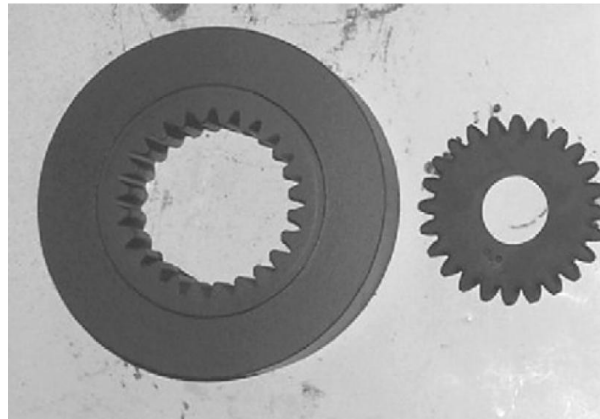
Exemple d'outillage fretté et pignon obtenu par forgeage (d'après Eyercioglu et al. [EYE, 09])
